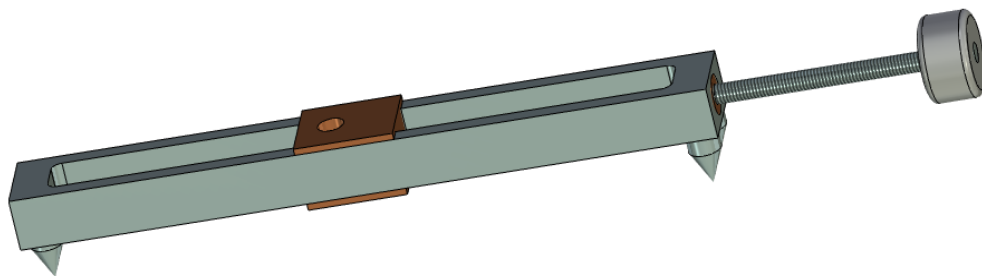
Деформометр для вимірювання стрілки прогину
